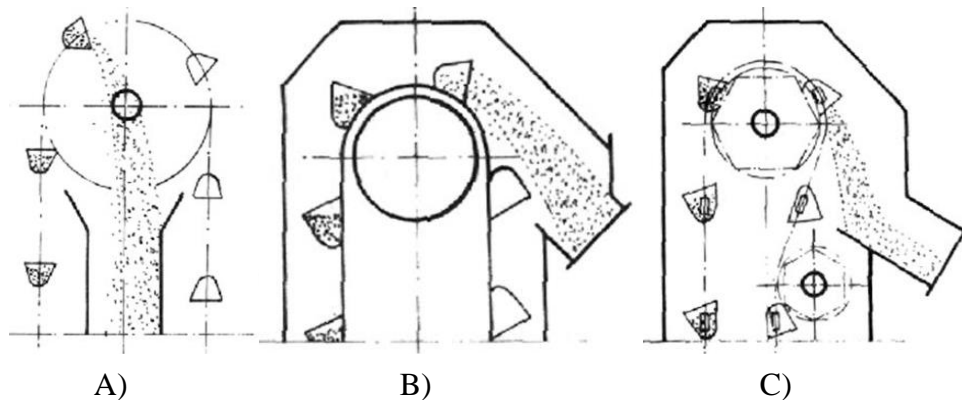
Tipos de descarga de elevador. A) Central B) Centrífuga C) Por Gravedad.
